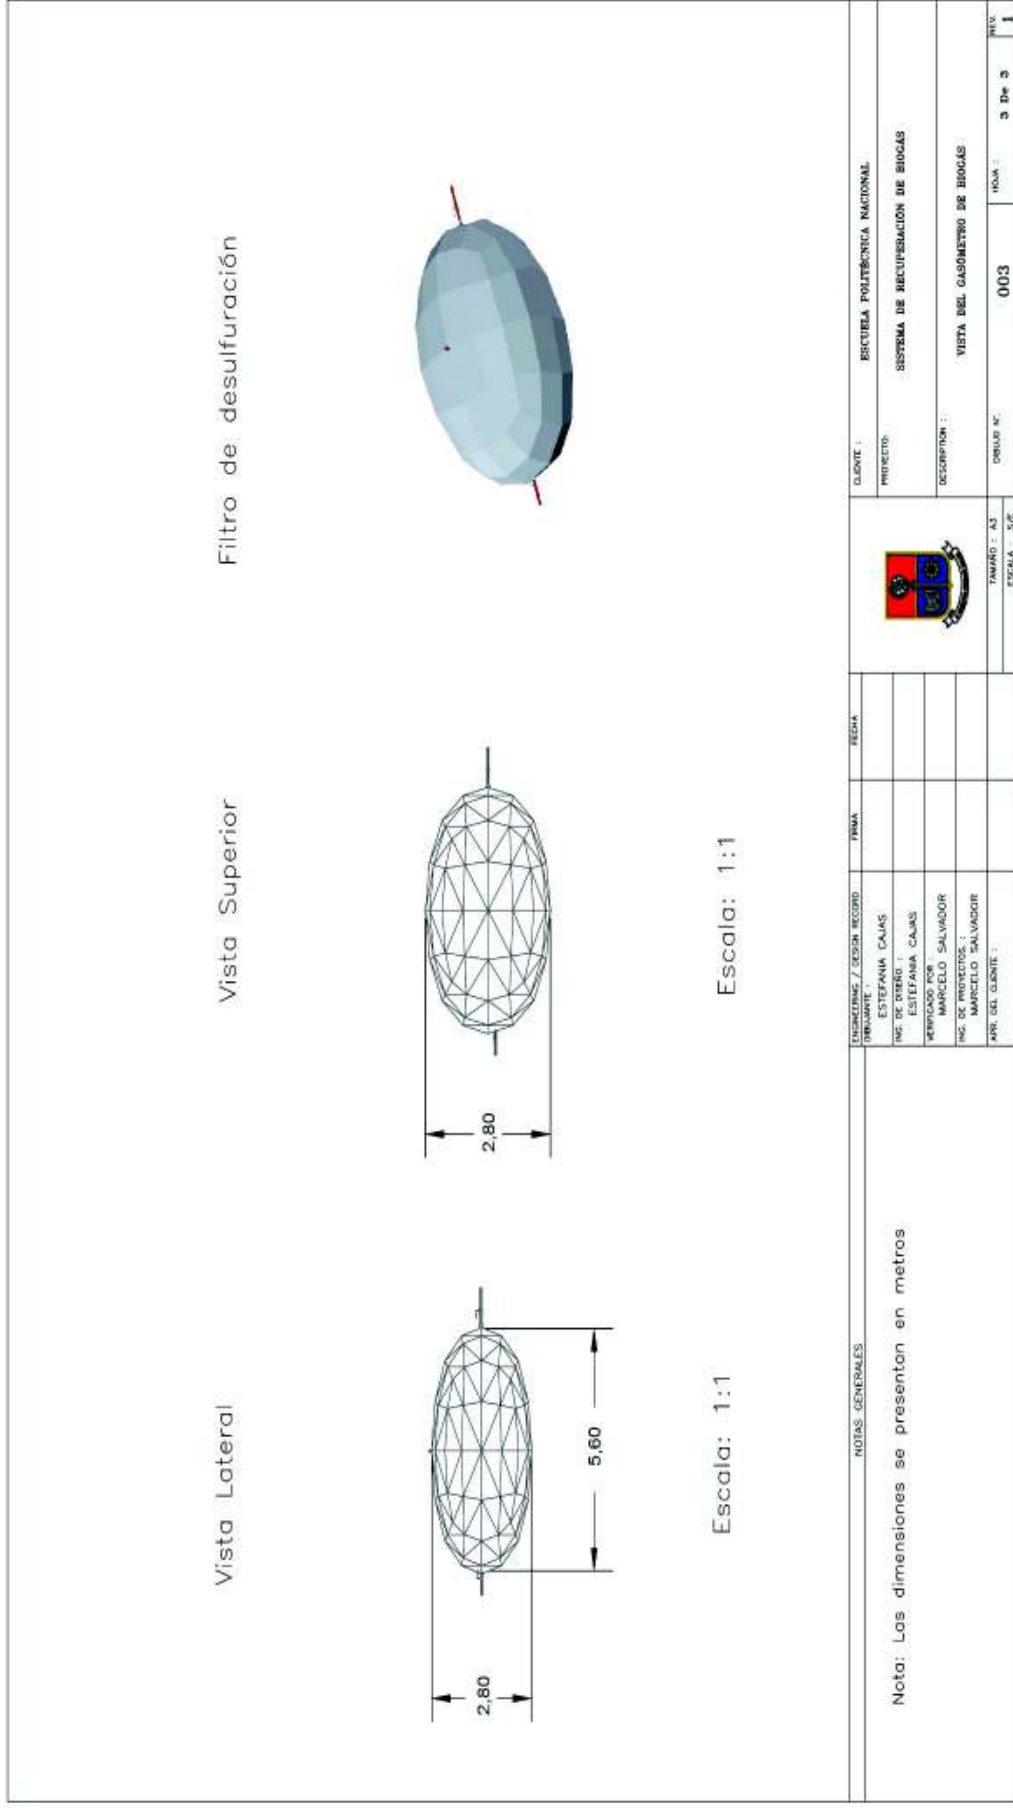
Plano de elevación del gasómetro de biogás (K-101)
